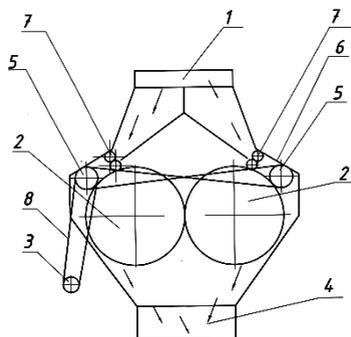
Фрезерно-валковый агрегат: 1- приёмный бункер; 2- барабаны; 3- электродвигатель; 4- разгрузочный бункер; 5- рабочие органы (фрезы); 6- корпус; 7- подающие валки; 8- ременная передача.
